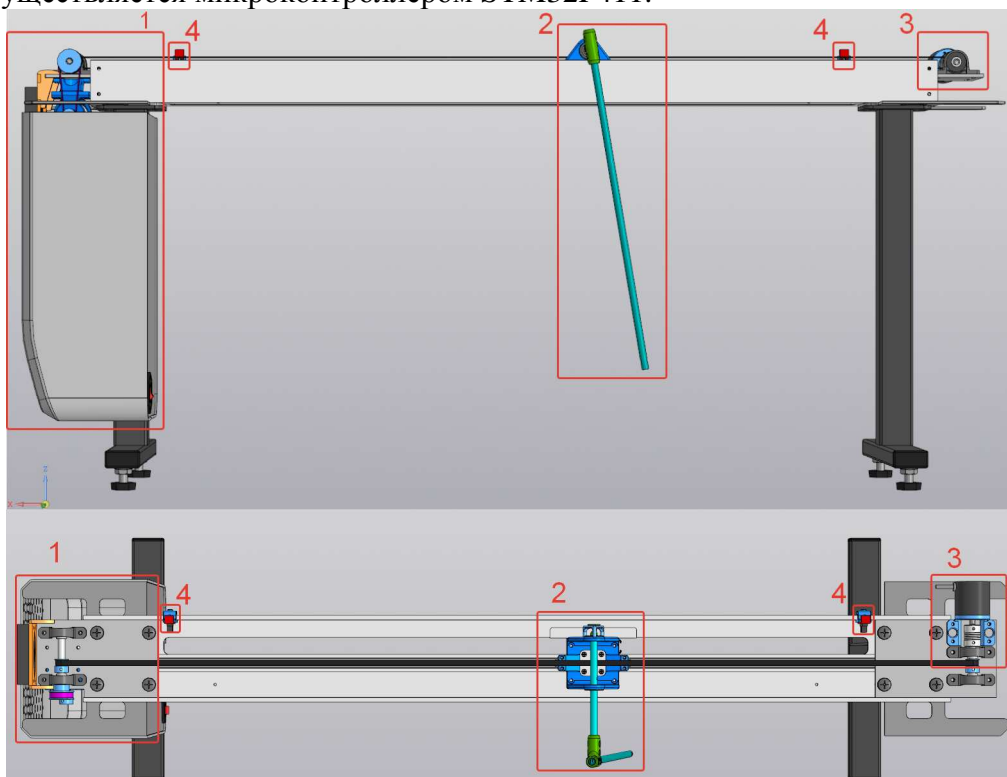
Конструкция стенда: 1 – блок управление и двигатель; 2 – каретка с маятником; 3 – инкрементный энкодер; 4 – концевые выключатели
